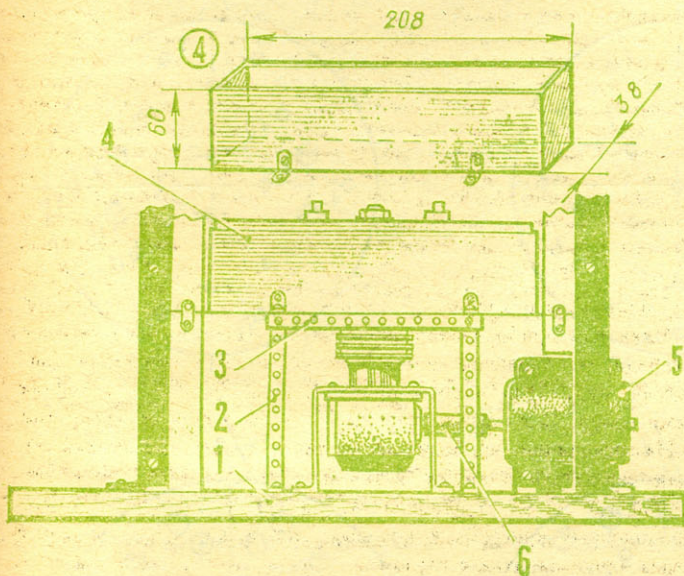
Конструкция вибратора: 1 — основание, 2 — стойка, 3 — П-образная деталь от «Конструктора» с микродвигателем, 4 — короб, 5 — электродвигатель от швейной машины, 6 — резиновая трубка.
